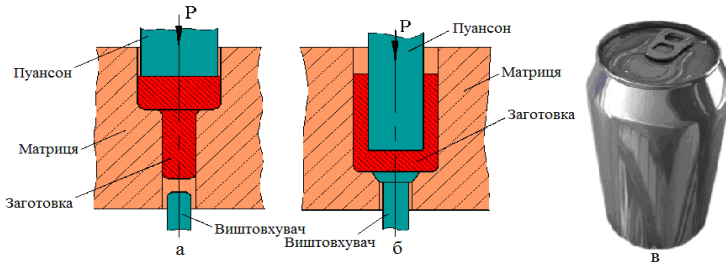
Штампування видавлюванням: а – пряме; б – зворотне; в – виріб
